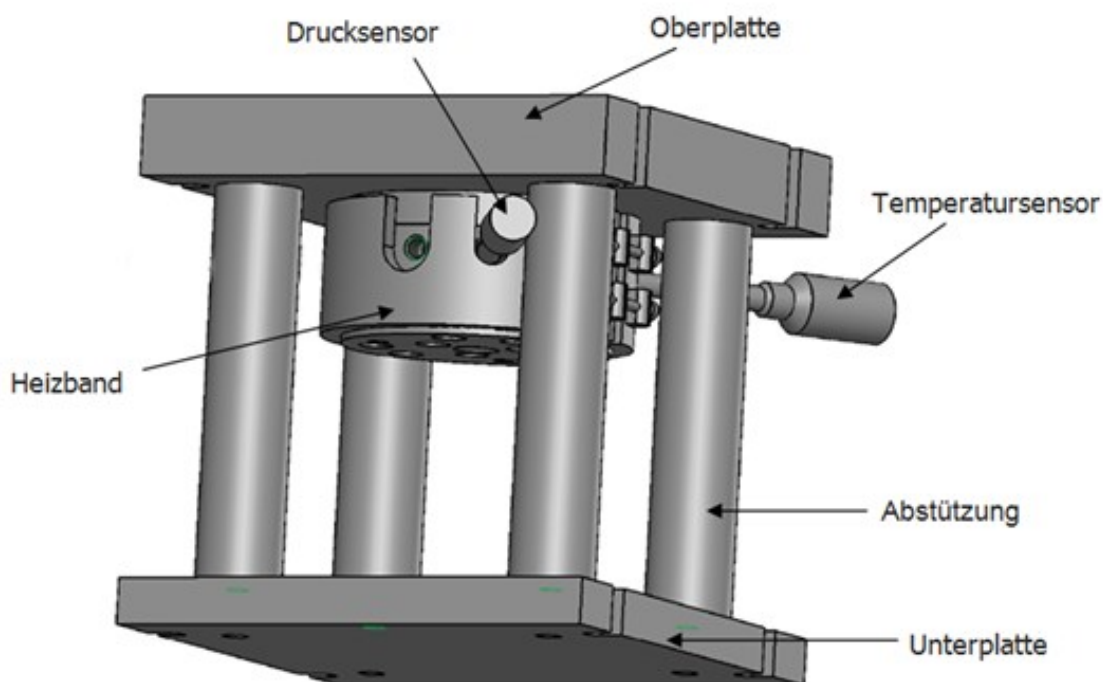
3D-Ansicht der Versuchswerkzeugs [20]
